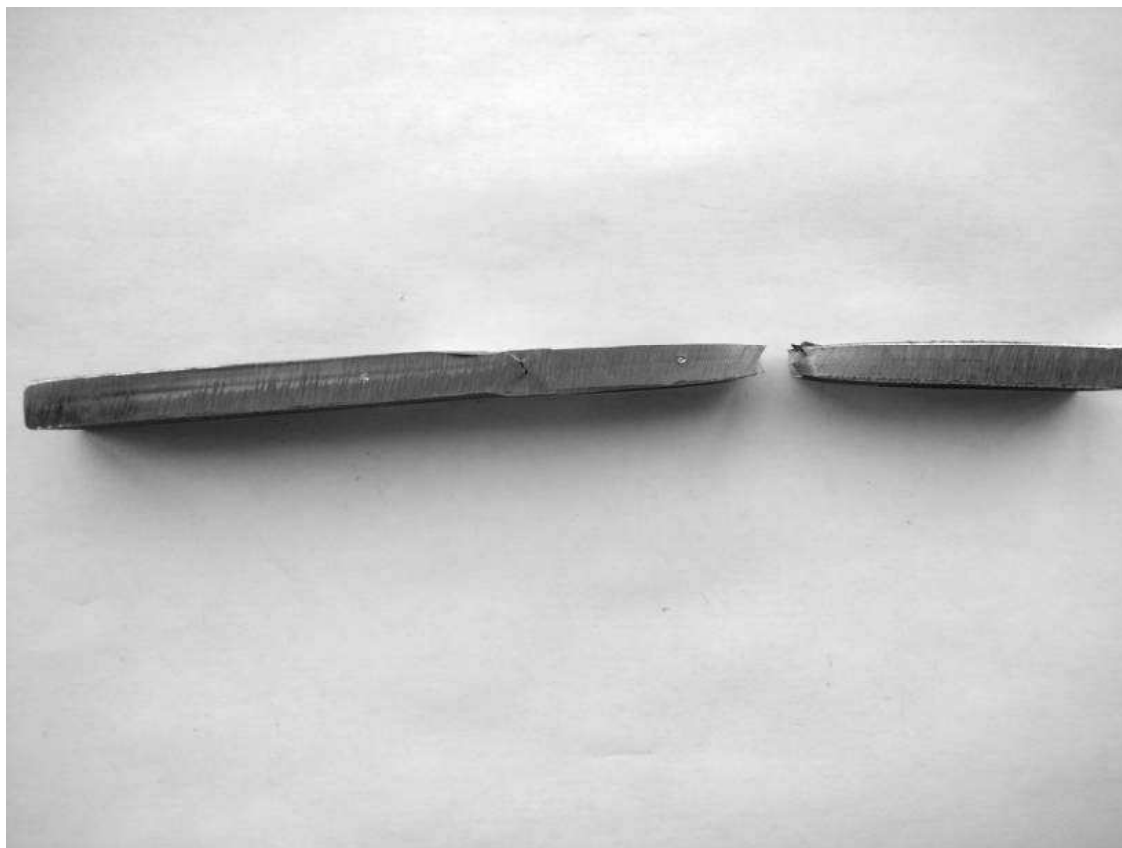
Образец WELDOX 700E + 09Г2С заваренные проволокой Св-08Г2С.
